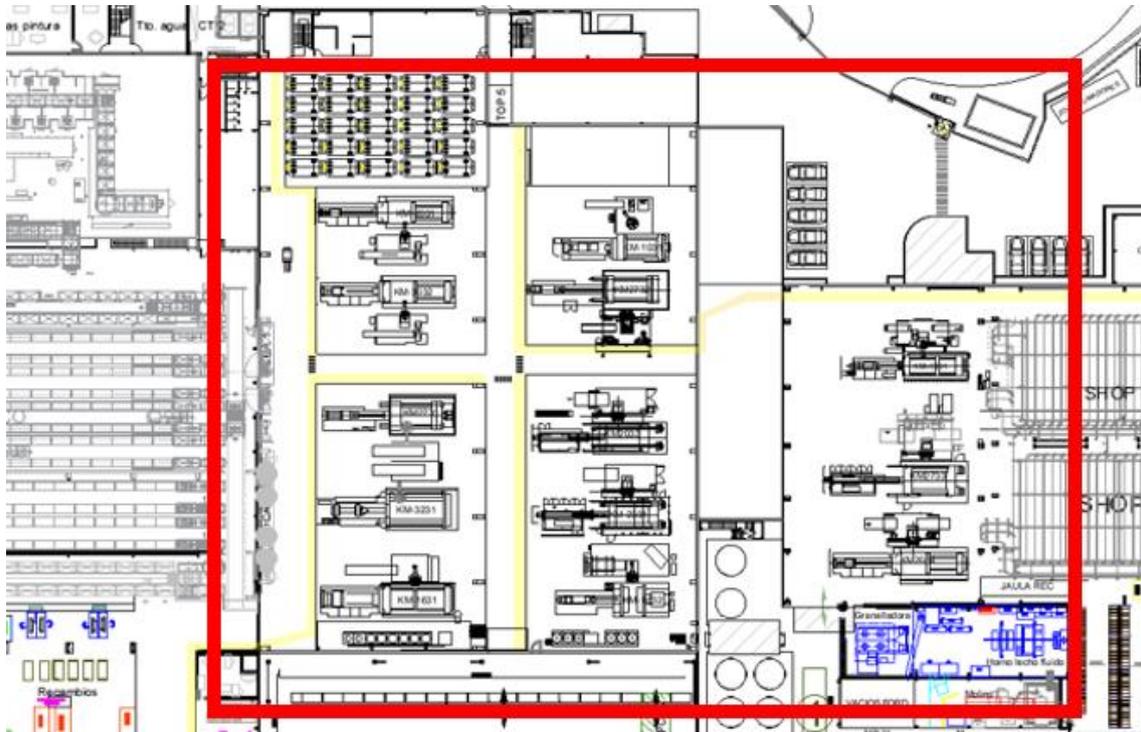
Layout zona de Inyección - Fuente: Documentación interna de la empresa (2021)
